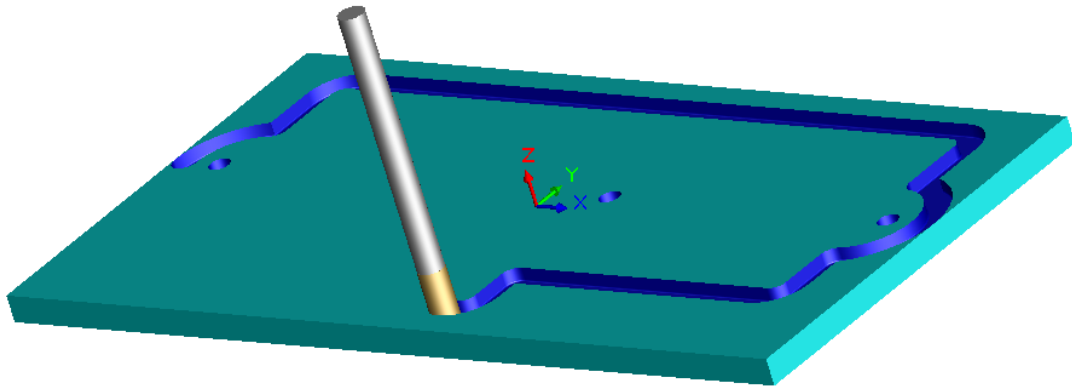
Перший прохід кінцевою фрезою Sandvik 2P340-0500-PA 1630
